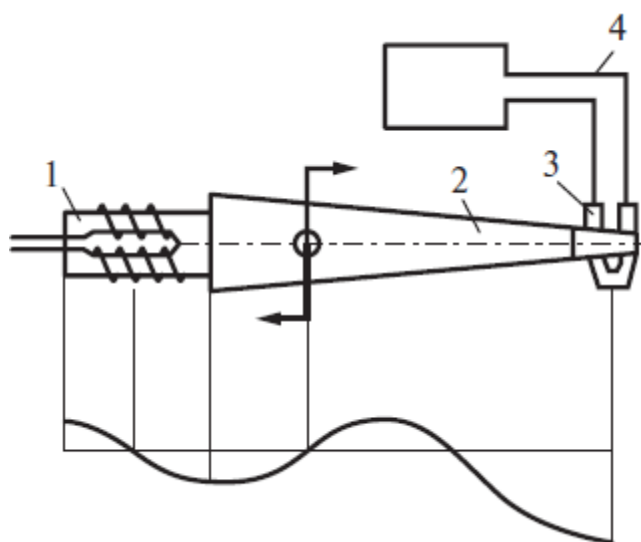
Схема термокомпрессионной сварки с наложением ультразвуковых колебаний
